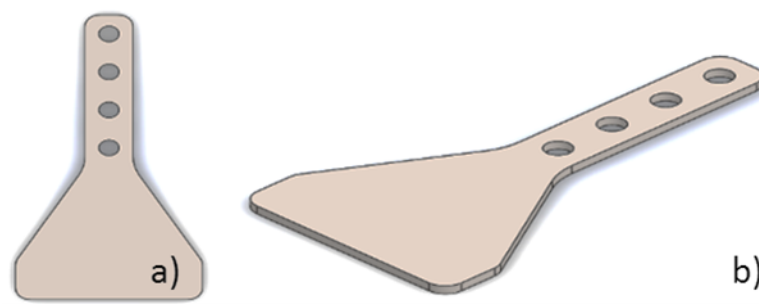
Placa de sujeción a) vista superior, b) vista isométrica.
